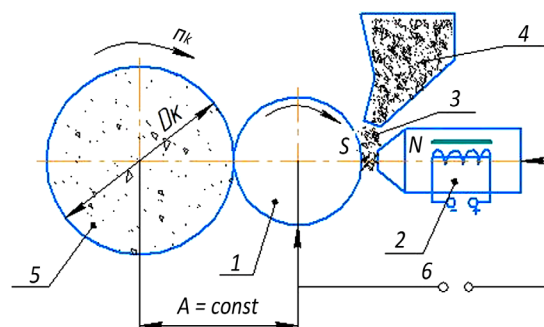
Схема комбинированной упрочняющей обработки наружных цилиндрических поверхностей МЭУ со шлифованием:
